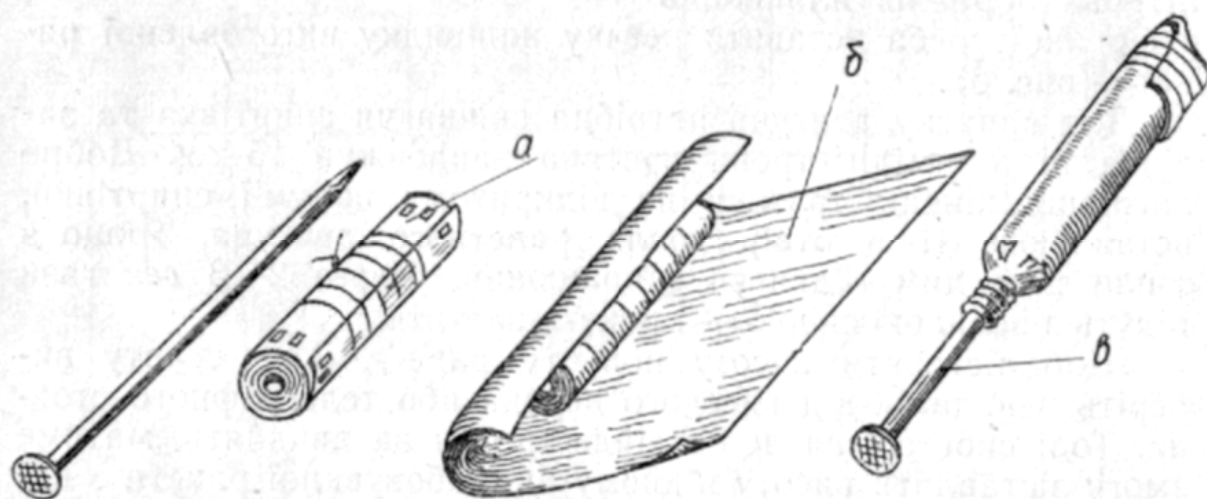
Виготовлення мікроракетного двигуна з кіноплівки: а) кіноплівка в рулончику; б) обгортання рулончика фольгою; в) цвях для формування сопла.
